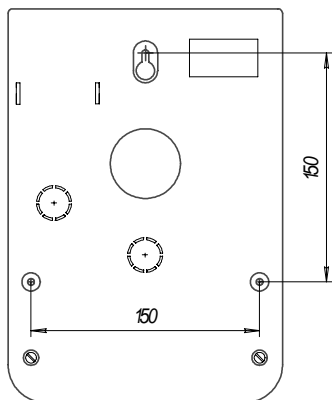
Расположение отверстий для крепления на основании оповещателя
